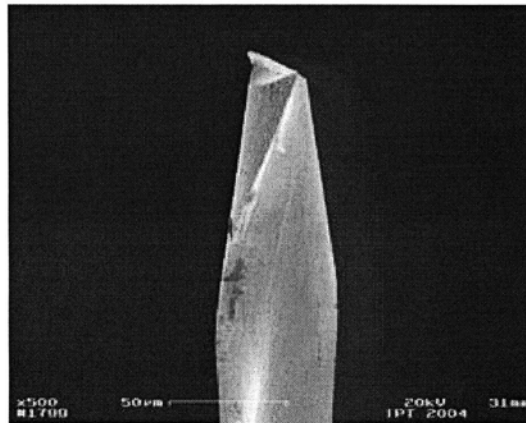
Інструмент Ø50 мкм для мікрофрезерування
